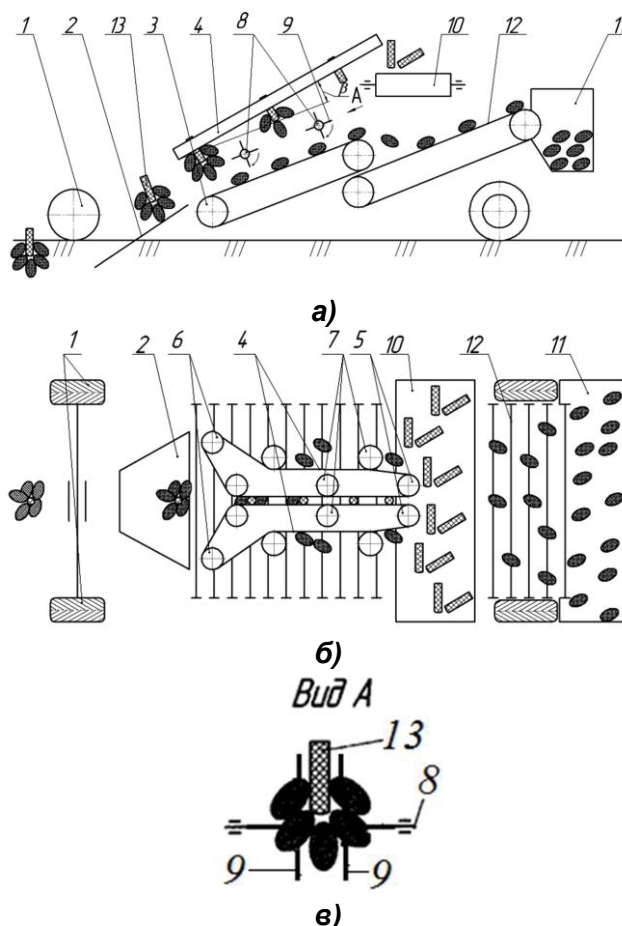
Машина для уборки клубней топинамбура: а – вид сбоку; б – вид сверху; в – вид по стрелке А.
